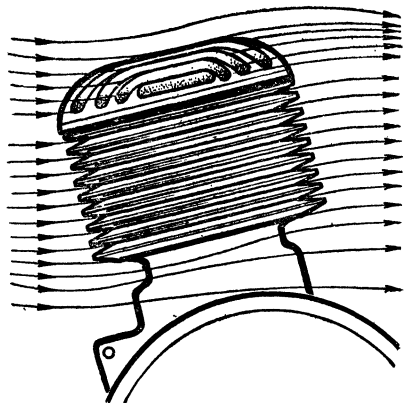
Схема воздушного охлаждения цилиндра двигателя.
